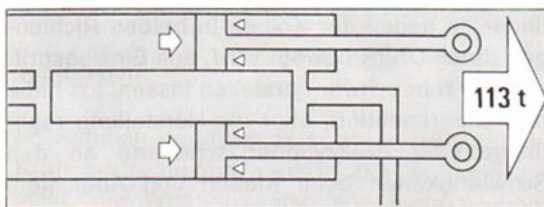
Schnittzeichnung zweier parallel gespeister Hydraulikzylinder.
